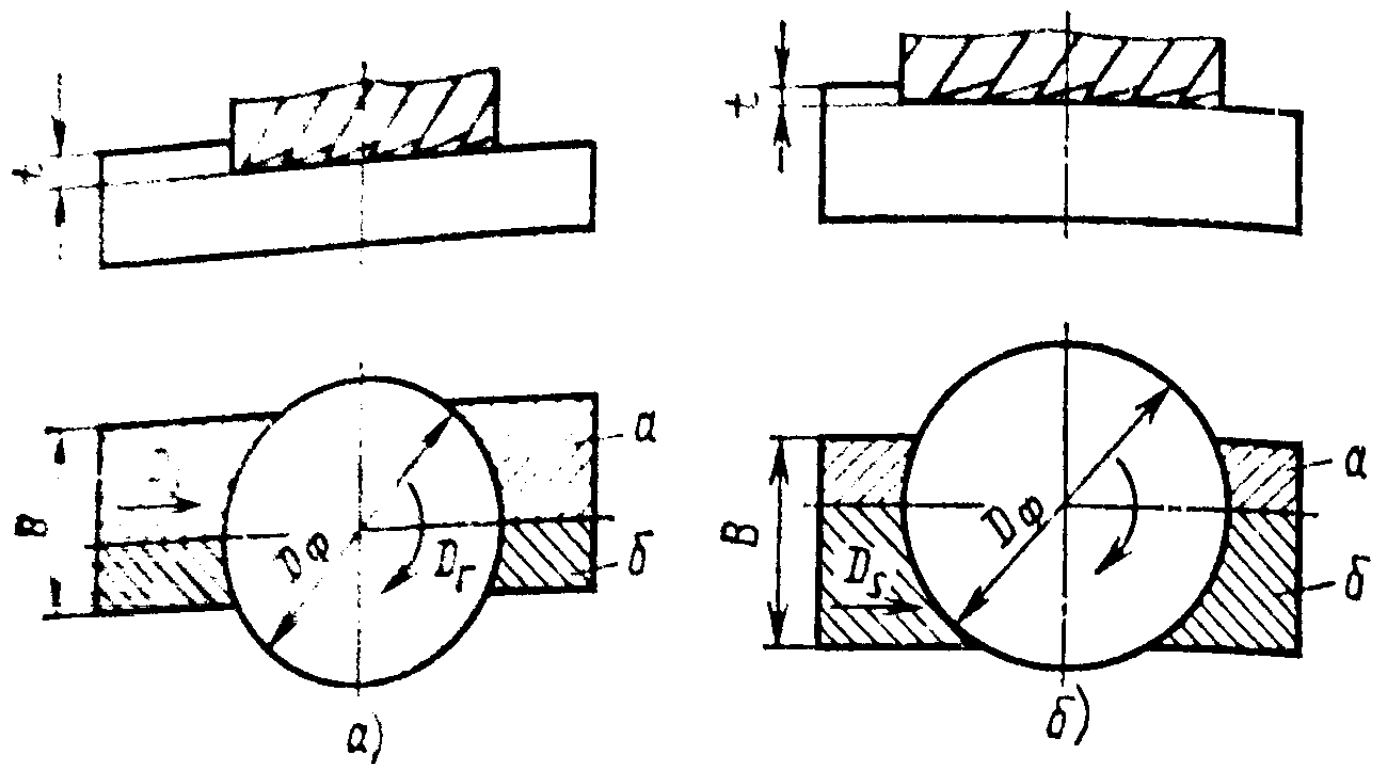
Попутное и встречное фрезерование торцовыми фрезами
